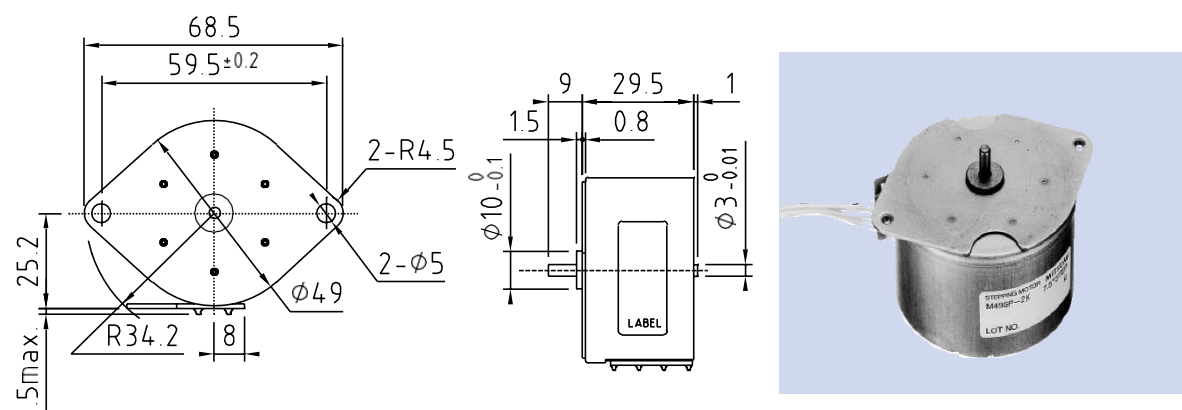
Dimensions de Moteur pas à pas (mm)
